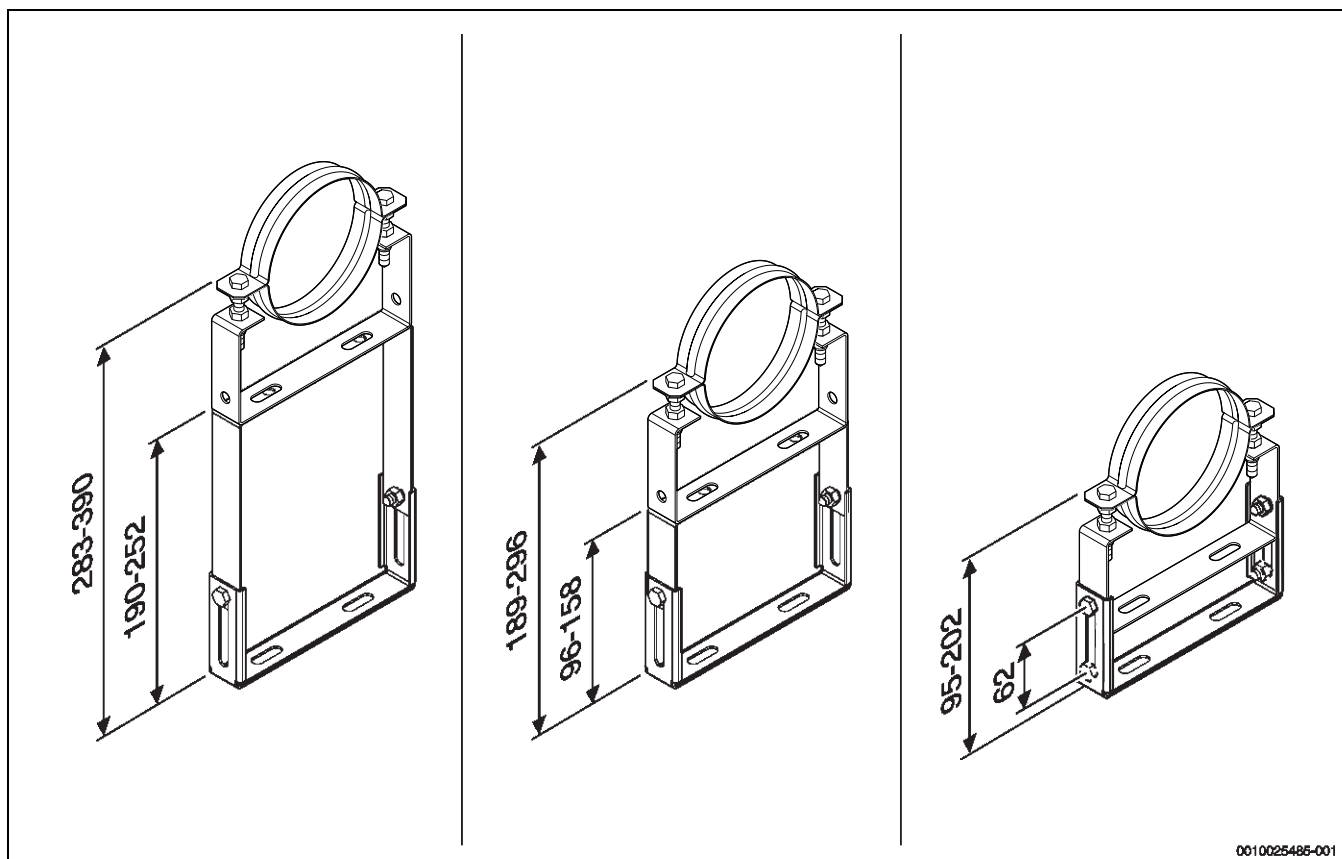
Verlängerung für Wandhalterung + Wandhalterung DN 125
